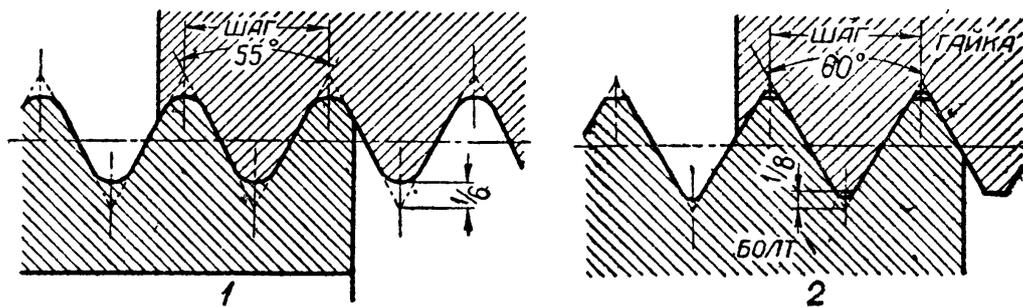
Типы резьб: 1—резьба Витворта; 2—резьба метрическая
